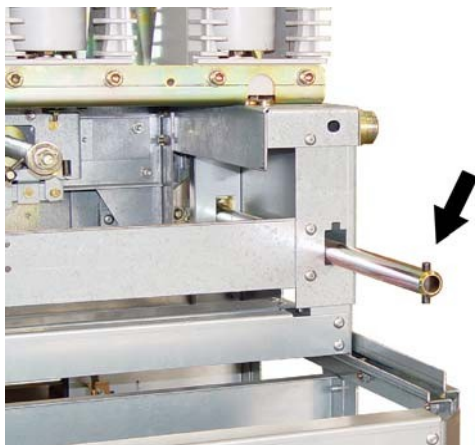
Соединительная шпилька вала управления заземляющего ножа
